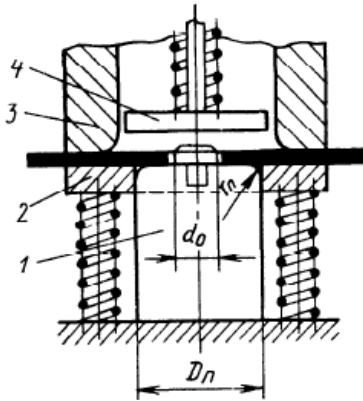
Схема отбортовки цилиндрическим пуансоном с плоским торцом: 1 – пуансон; 2 – съёмник; 3 – матрица; 4 – выталкиватель
